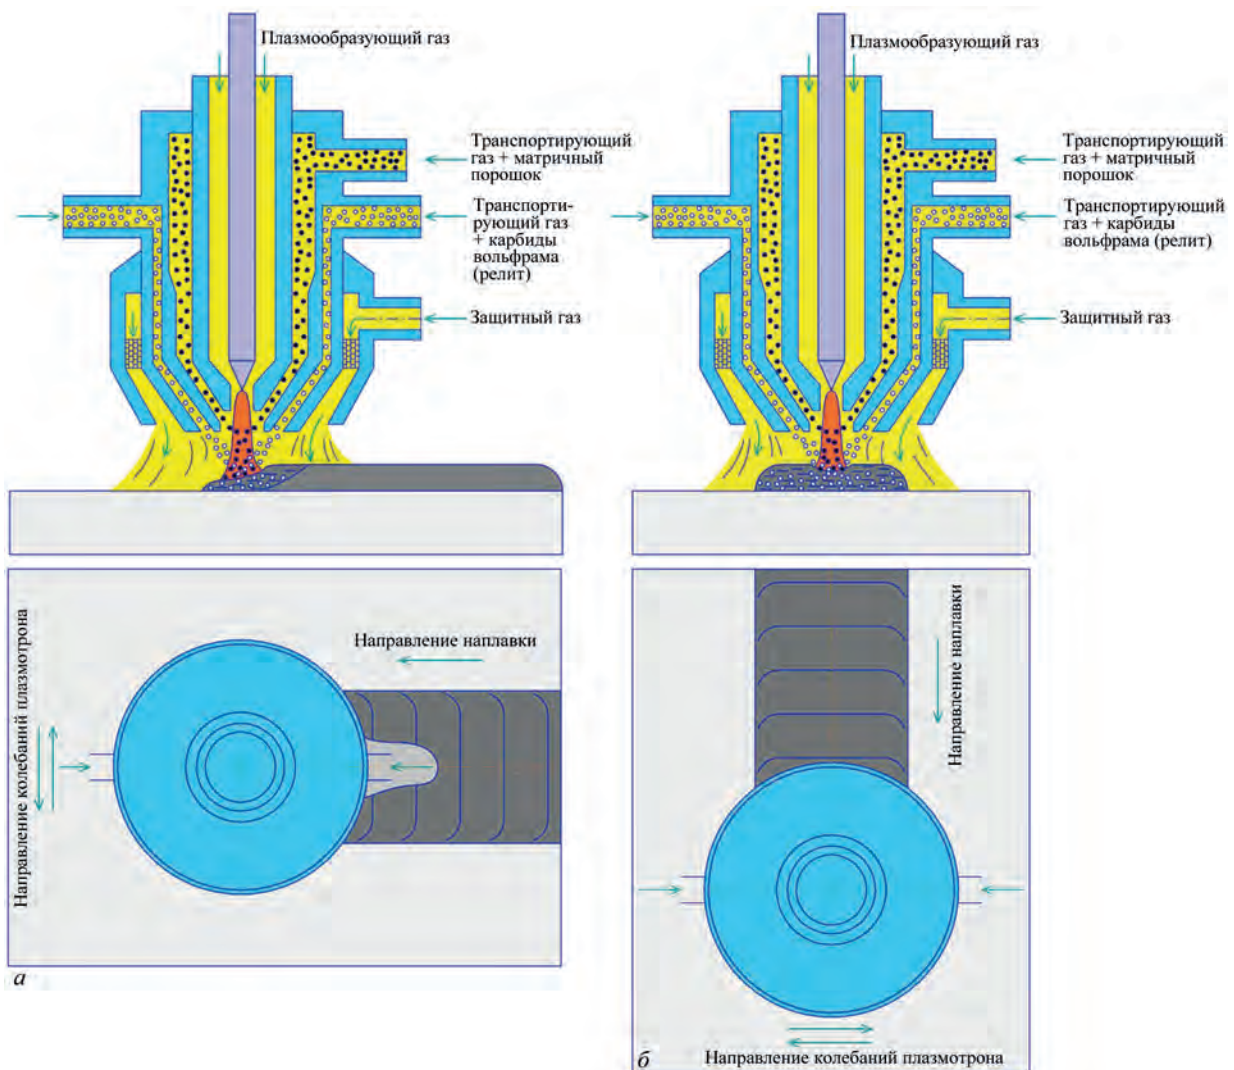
Схемы плазменно-порошковой наплавки с подачей релита в головную часть сварочной ванны через два канала: а – каналы расположены в плоскости параллельно оси наплавляемого валика; б – перпендикулярно оси
